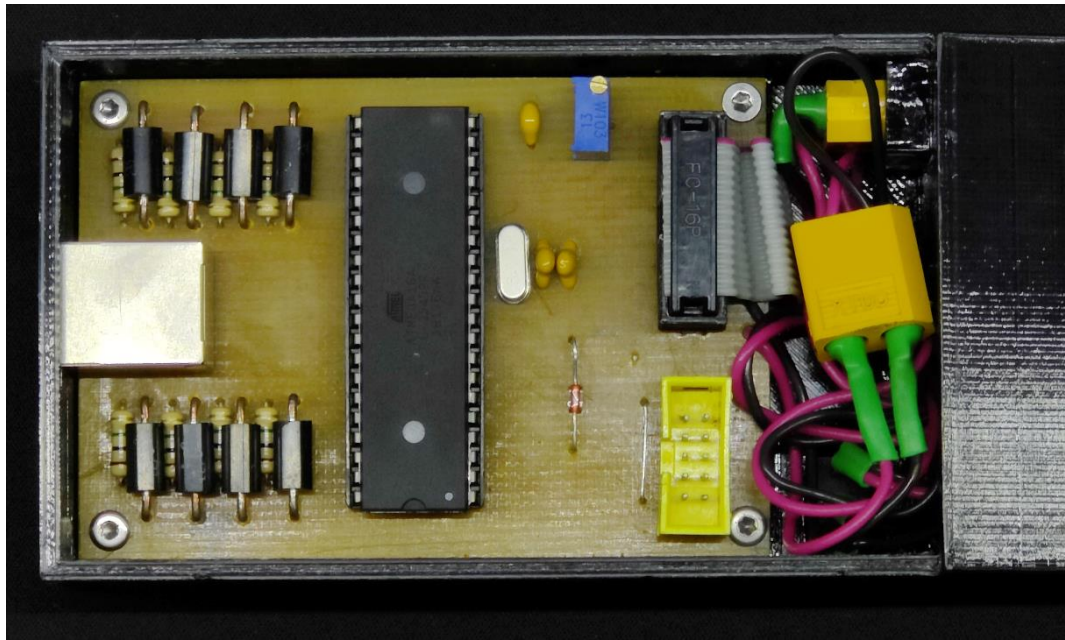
Друкована плата з верхньої сторони в корпусі.
